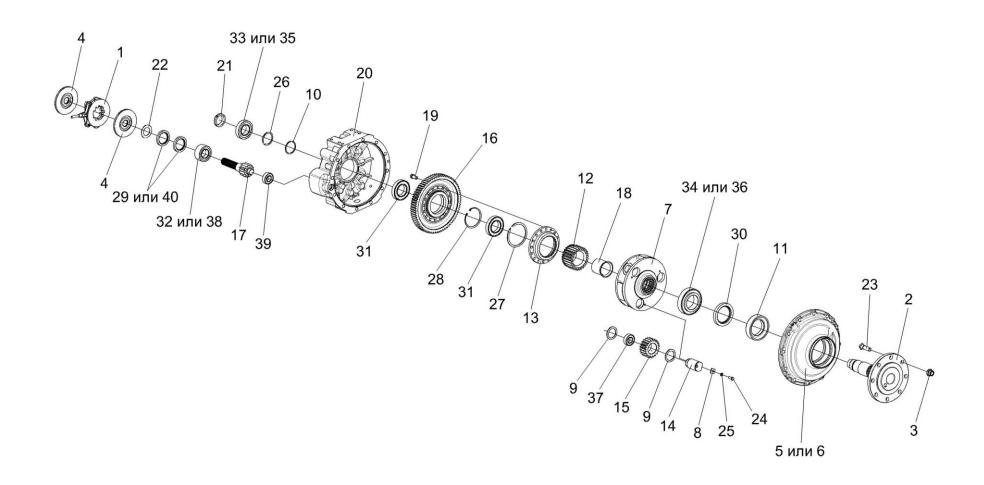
Редуктор правый МК-23М.04.000-03 (валы, шестерни)
